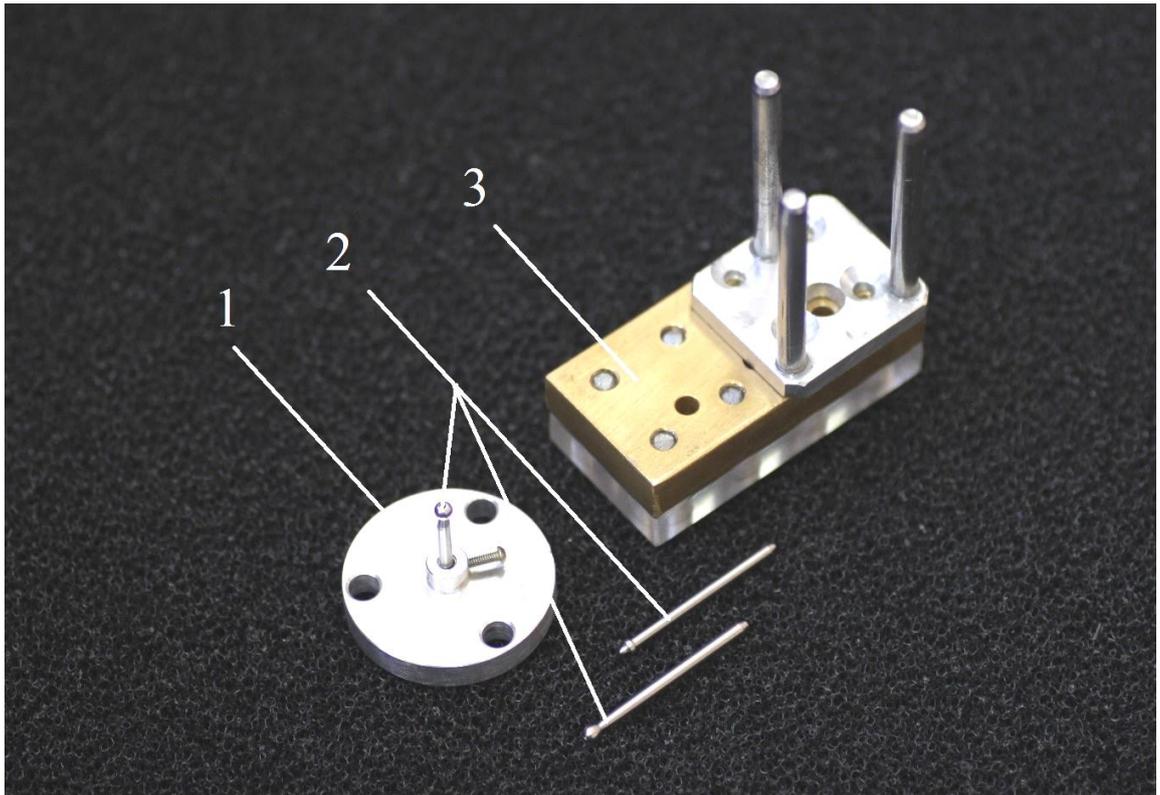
Внешний вид тестовой площадки с закреплёнными на ней направляющими для подвижного модуля: 1 - подвижный модуль; 2 - исследуемые штопферы с различной формой рабочей поверхности; 3 - тестовая площадка
